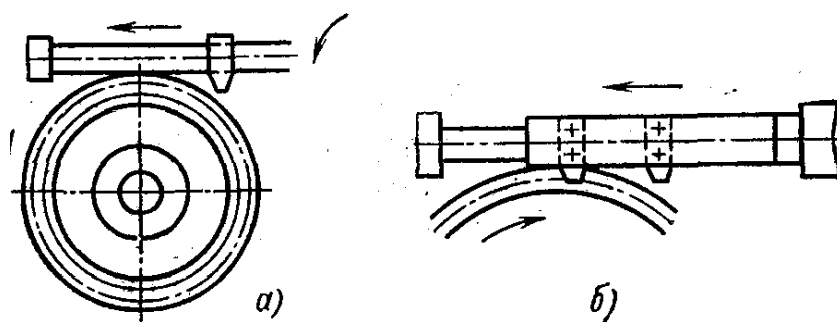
Схеми зубонарізання черв'ячних зубчастих коліс різцями
